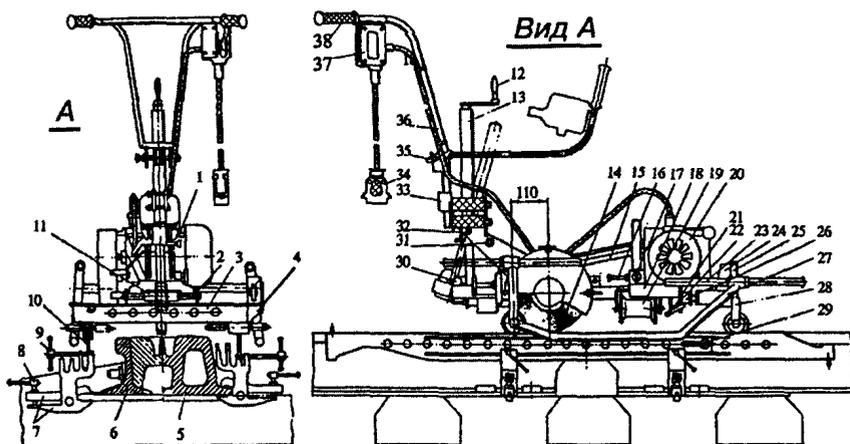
Устройство рельсошлифовального станка 1649
